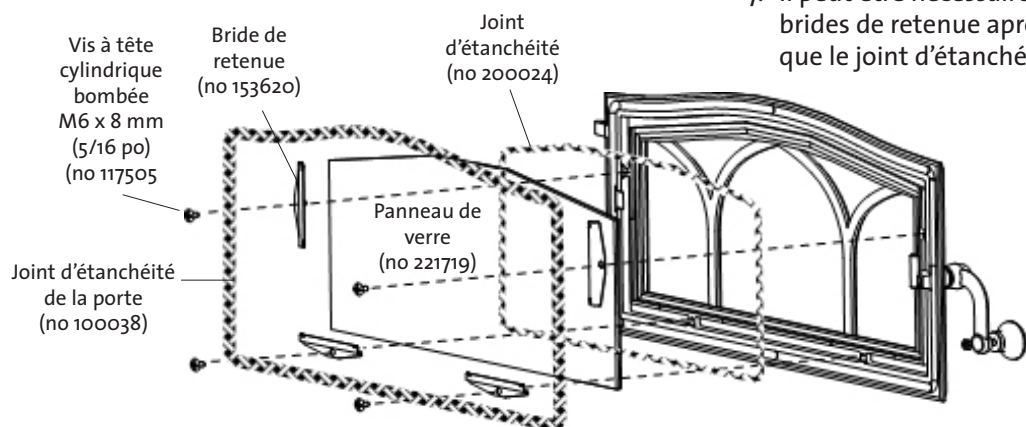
Pièce de remplacement de la porte de verre et des joints d'étanchéité.
